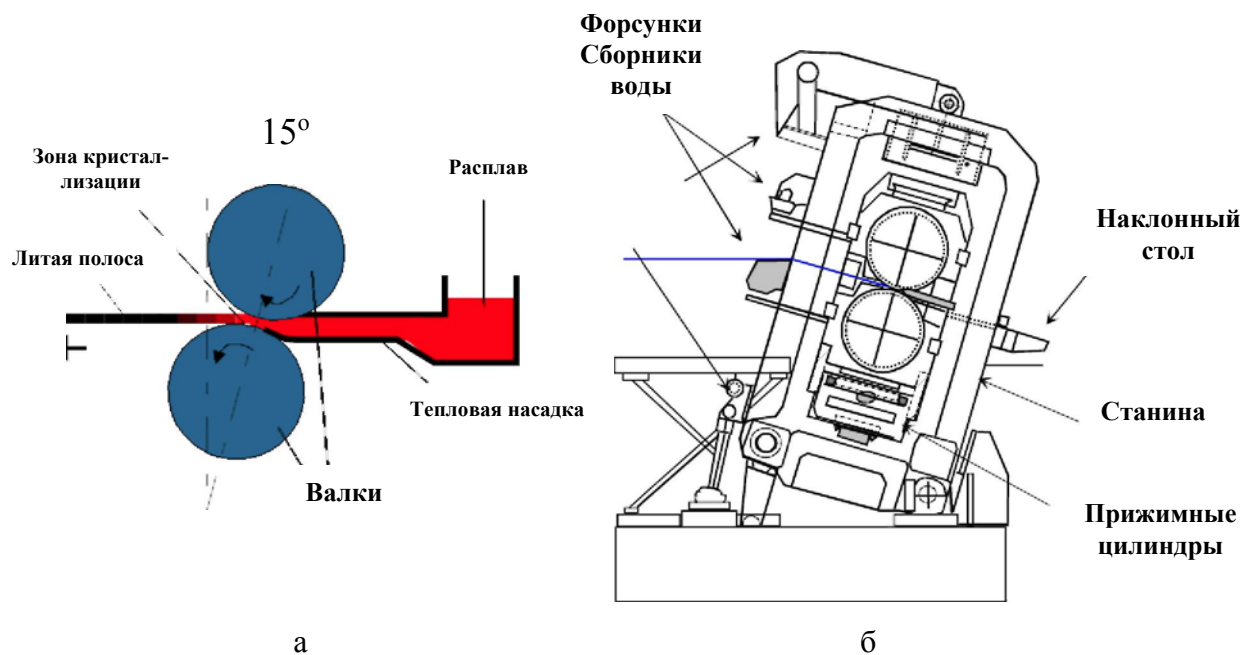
Конструкция агрегата беслитковой прокатки компании Fata-Hunter:
